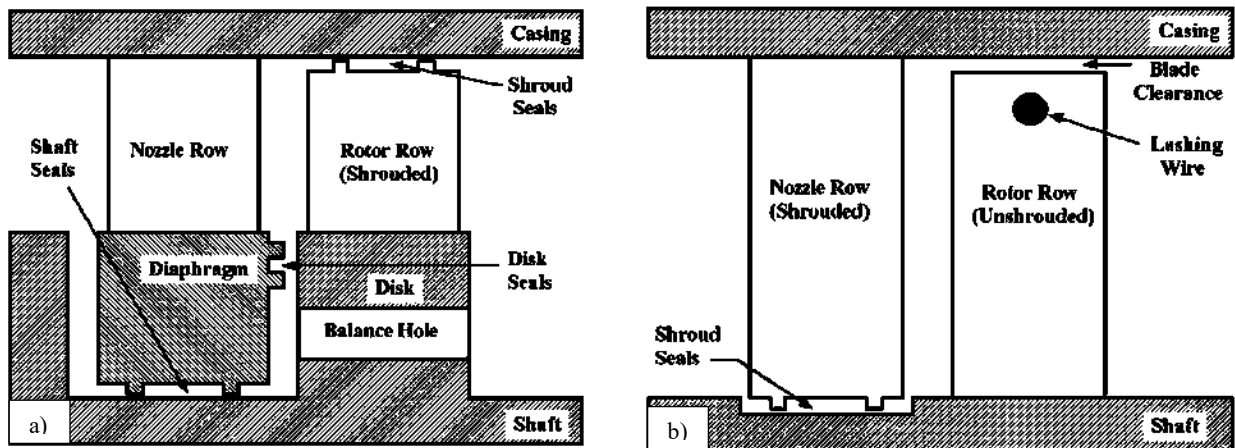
Turbina de flujo axial disco-diafragma (a) y tambor-rotor (b) [23].
